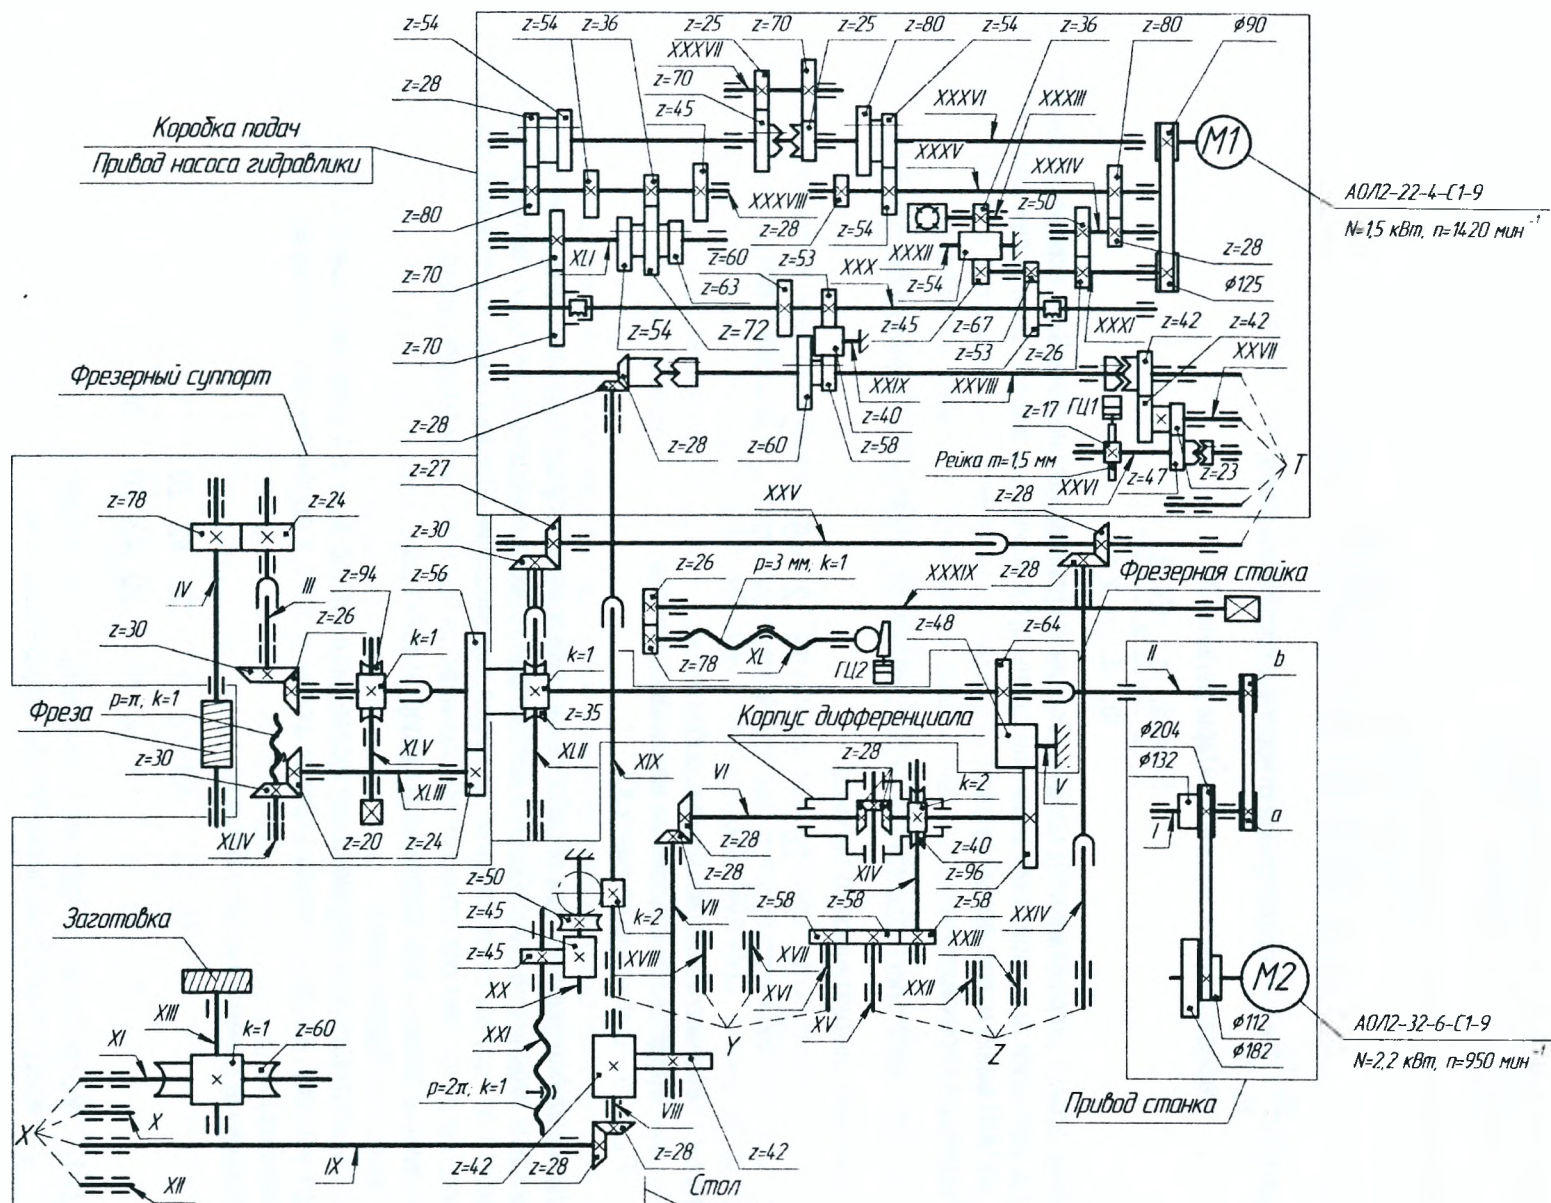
Кинематическая схема зубофрезерного станка 5K301П
